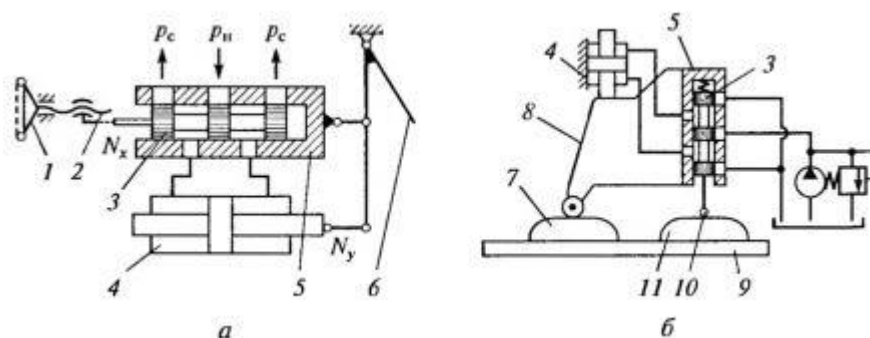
Следящие гидроприводы: а - рулевого управления колесной транспортной машины; б - фрезерного гидрокопировального
